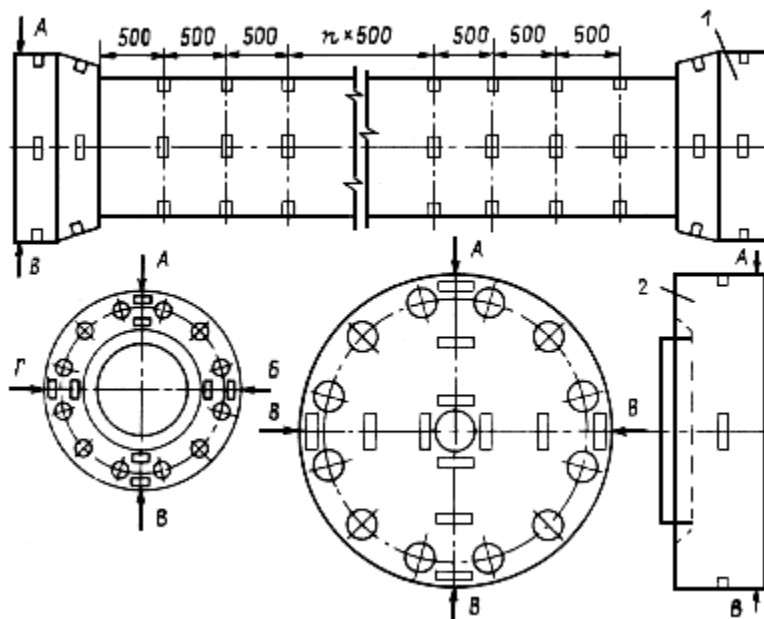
Места замера твердости на корпусах и крышках сосудов, подвергшихся аварийным температурным воздействиям: 1 - корпус; 2 - крышка
